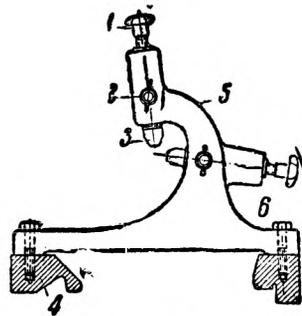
Расточка отверстия с поддержкой обрабатываемой детали лунетом.
